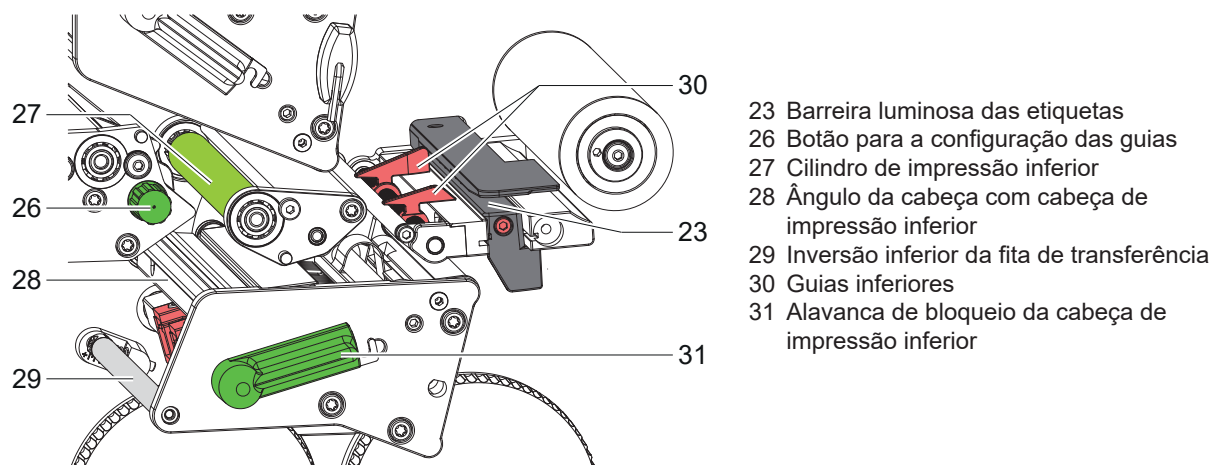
Mecanismo de impressão - módulo de impressão inferior
